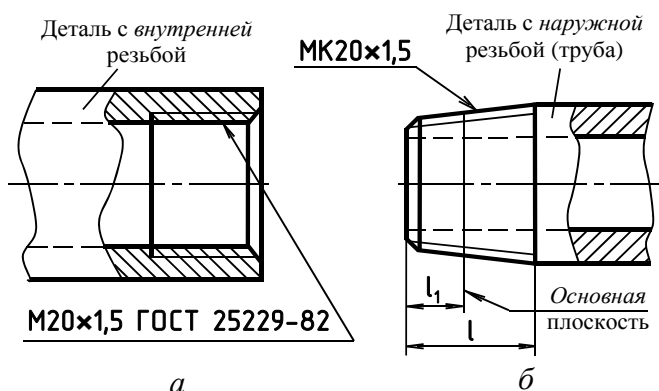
Обозначение на чертеже внутренней цилиндрической резьбы с профилем по ГОСТ 9150–2002 (а), соединяемой с наружной метрической конической резьбой (б) по ГОСТ 25229–82
